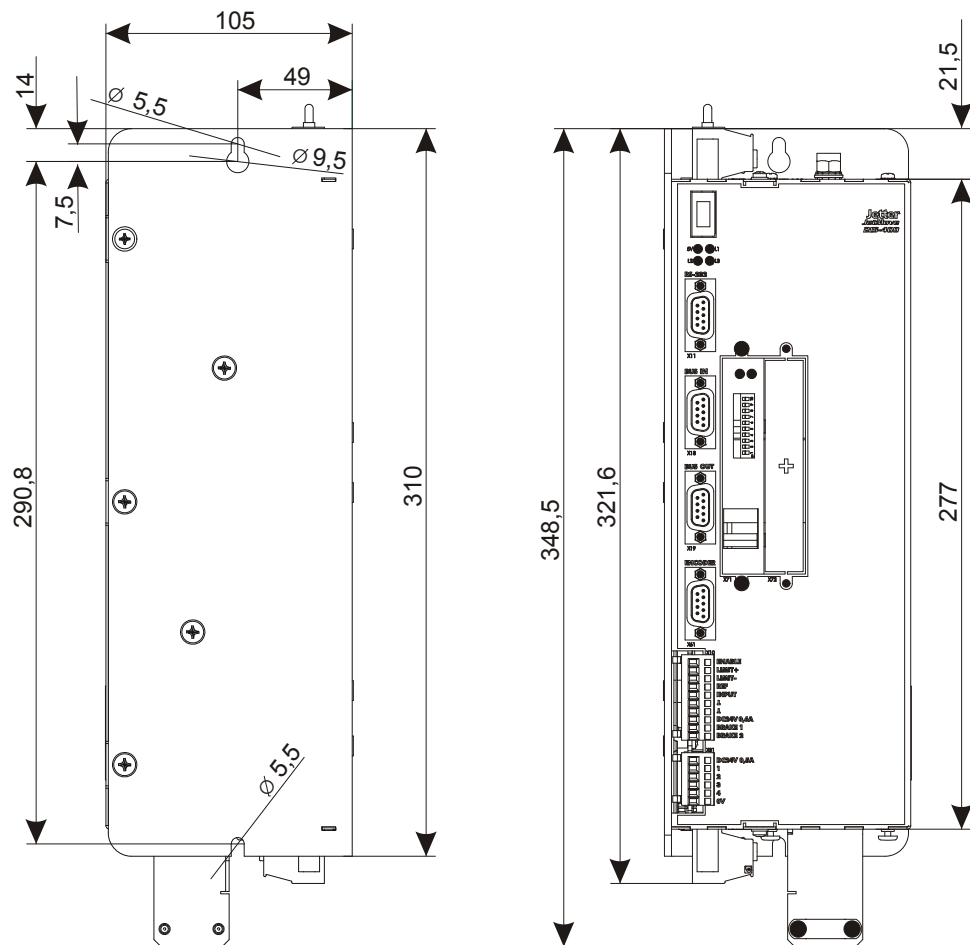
Rück- und Frontansicht des Gehäuses des JetMove 225-480 mit Bohrungen
